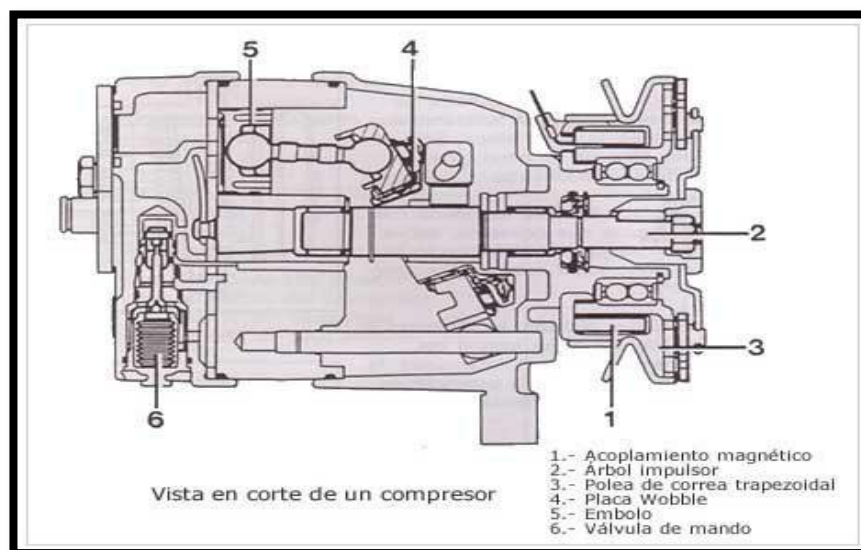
VISTA EN CORTE DE UN COMPRESOR
